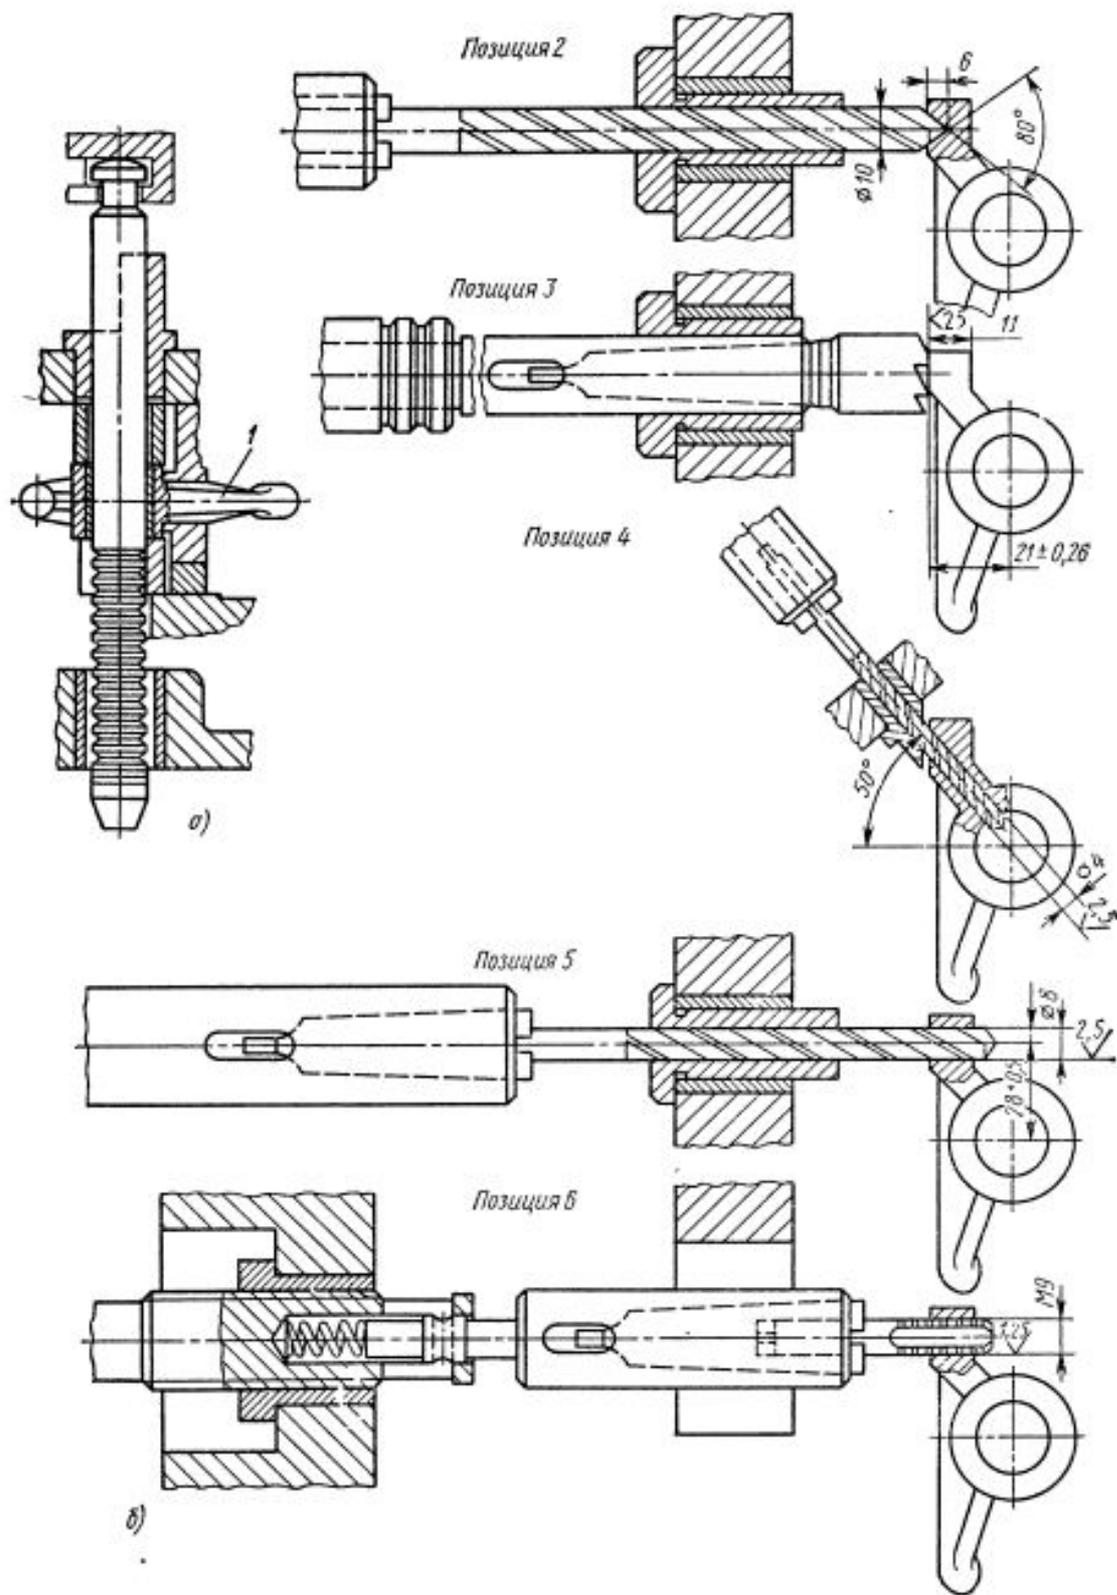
Схемы обработки заготовок на завершающих операциях изготовления коромысел клапанов
